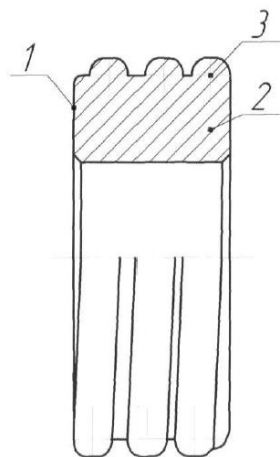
Ролик для обкочування металевих циліндричних деталей
